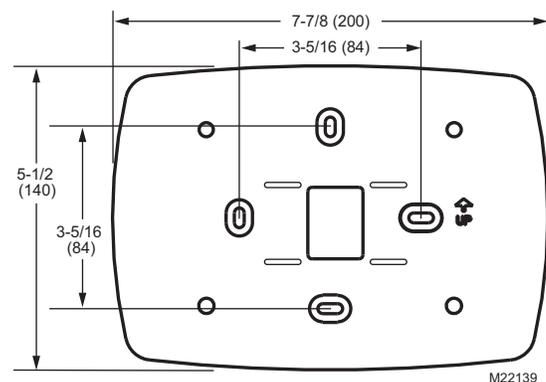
Placa de cubierta 32003796-001. Dimensiones en pulgadas (mm).
